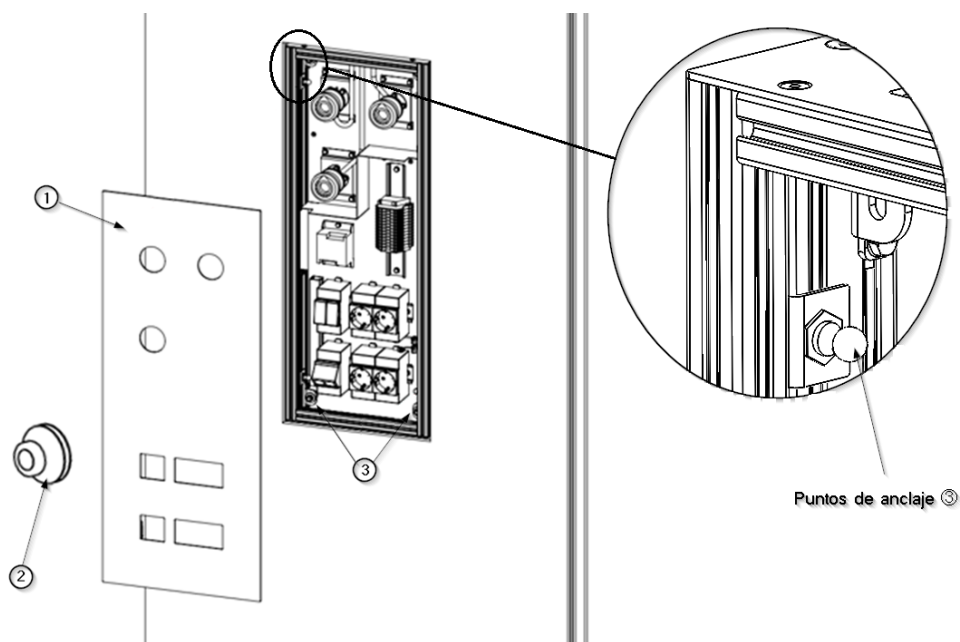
Entfernen der Frontabdeckung des ANTEA
